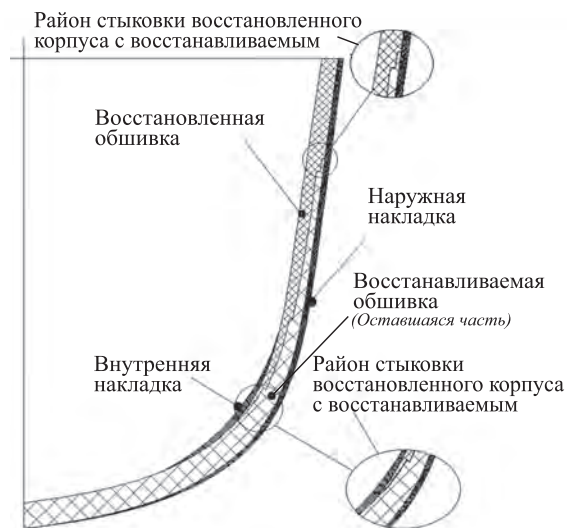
Принципиальная схема восстановленной обшивки корпуса
